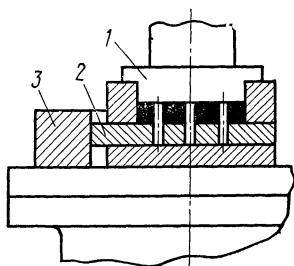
Схема ориентирования с помощью приспособления для пайки:
